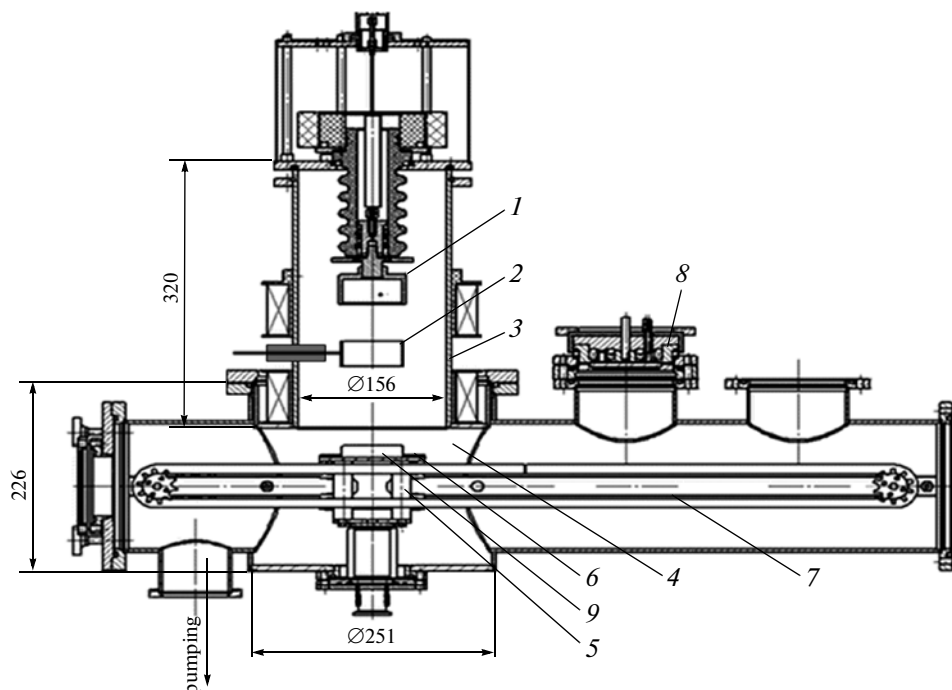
Общий вид установки РИТМ-СП. 1 – взрывоэмиссионный катод; 2 – анод; 3 – корпус пушки; 4 – вакуумная камера; 5 – медный стержень; 6 – рабочий стол; 7 – цепная передача; 8 – магнетрон; 9 – образец.
